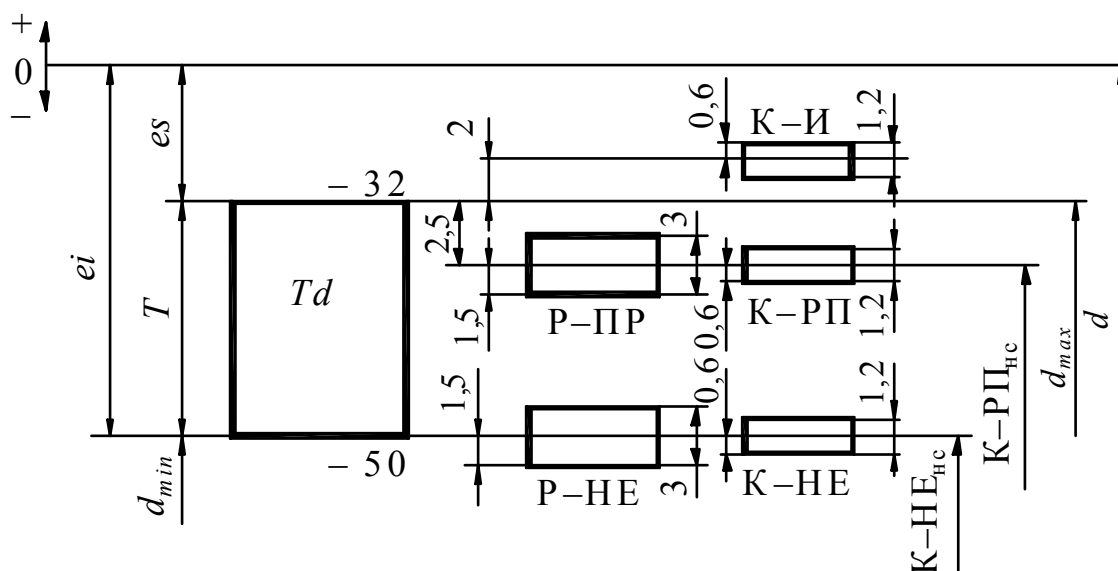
Схема расположения полей допусков предельных калибров для контроля валов
